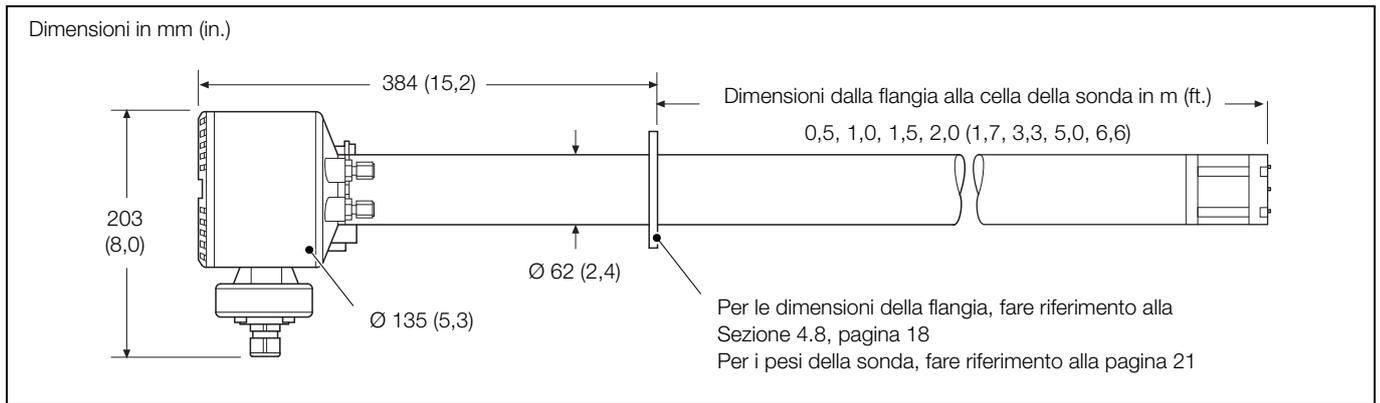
Dimensioni complessive – sonda Endura AZ30 remota
